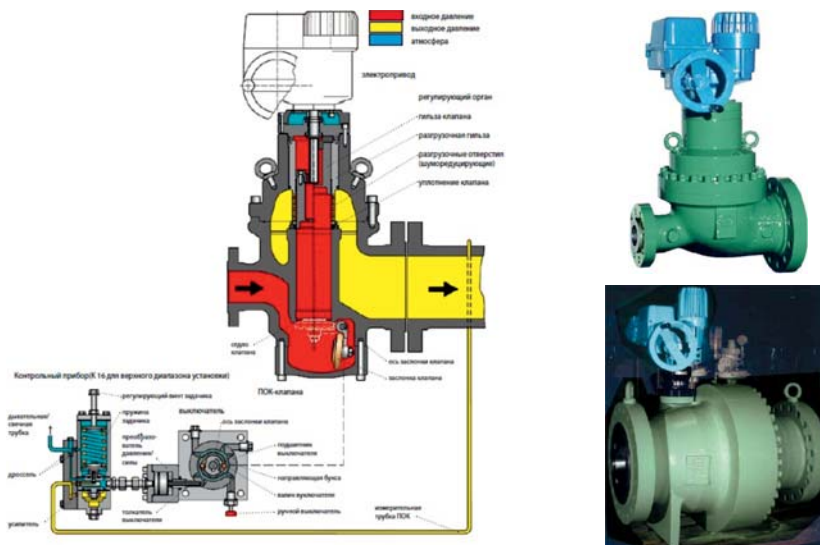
Внешний вид и устройство регулятора давления газа RMG 530-E и RMG 530-WG
